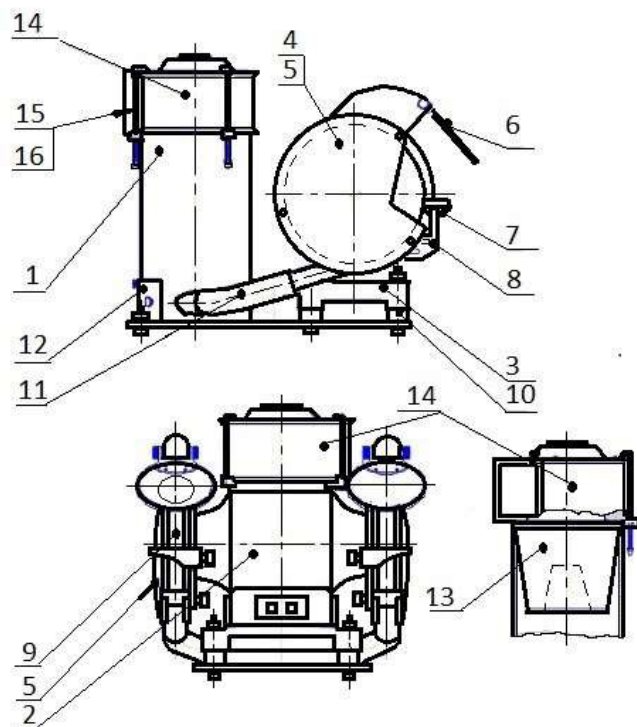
Общий вид заточного станка ЗСВ20 с вытяжкой:
